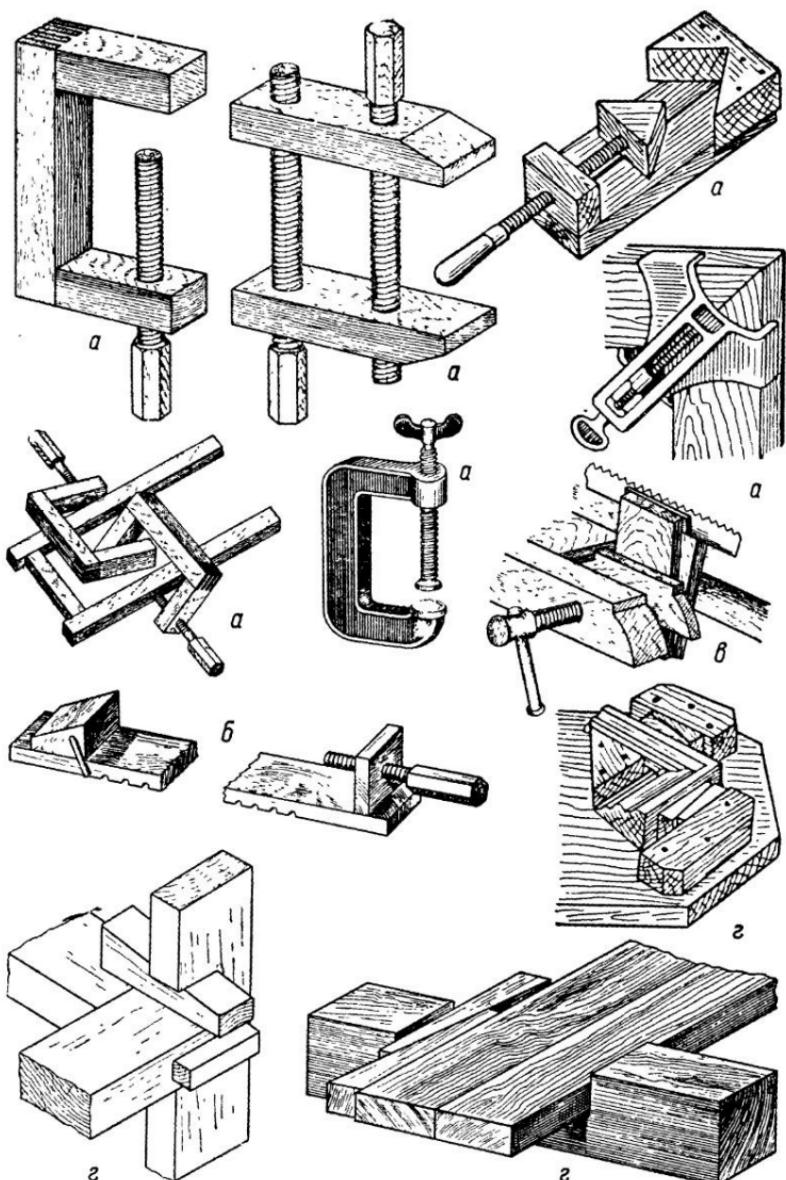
Приспособления к верстаку: *а* — струбцинки; *б* — цвинки,
